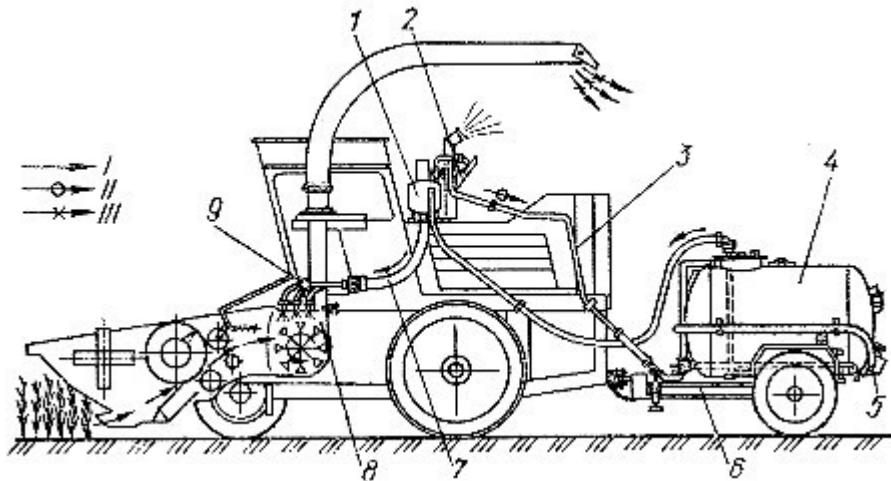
Схема агрегату для внесення рідких хімічних консервантів АВК-Ф-2: 1 – нагромаджувач; 2– ежектор; 3 і 7—шланги; 4– резервуар; 5 – заправний рукав; 6 – рама з ходовою частиною; 8– датчик маси; 9 – дозатор; I – консервант; II – вихлопні гази; III – рослинна маса.
